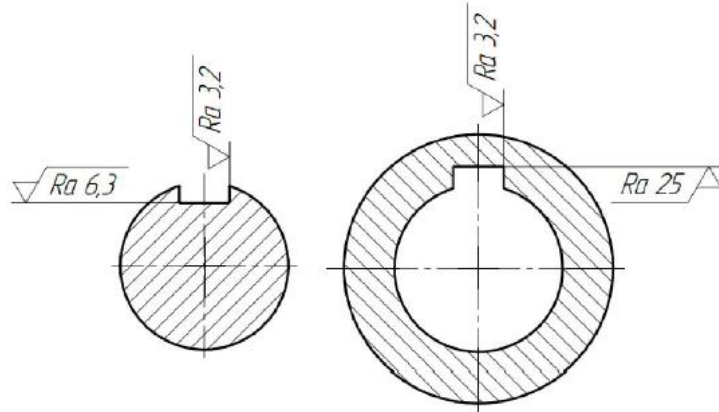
Шорсткість поверхні шпонкового паза вала та втулки
